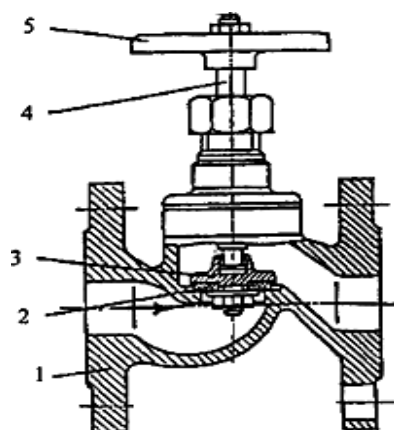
Вентиль запорный фланцевый: 1 - корпус; 2 - уплотнительное кольцо; 3 - золотник; 4 - шпindelь; 5 – маховик
